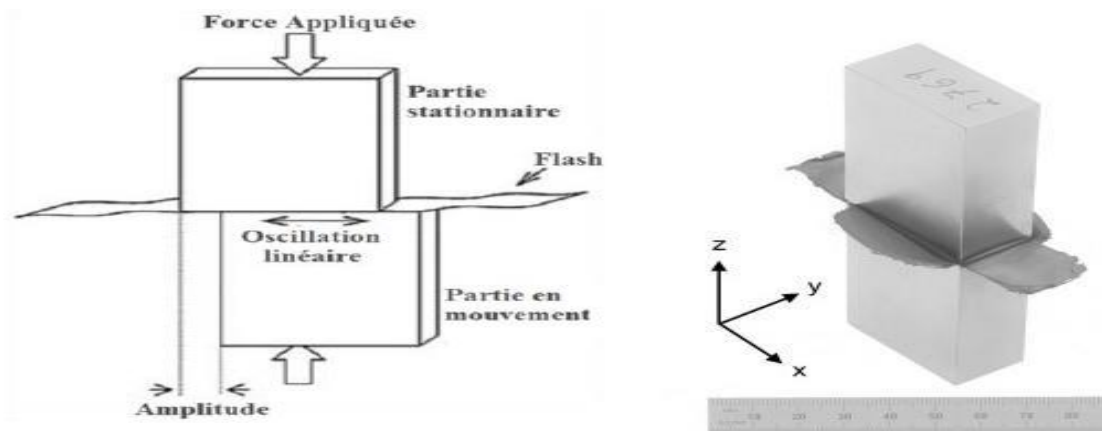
Illustration schématique du Procédé de soudage par friction linéaire [6].
